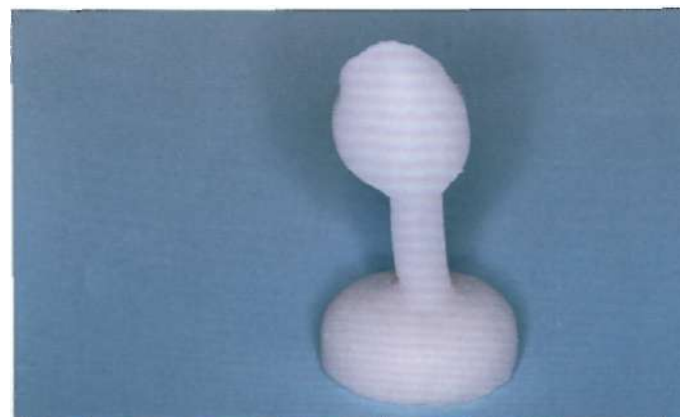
Отлитая коронка Empress, прикрепленная к керамической «пуговке» заготовкой
